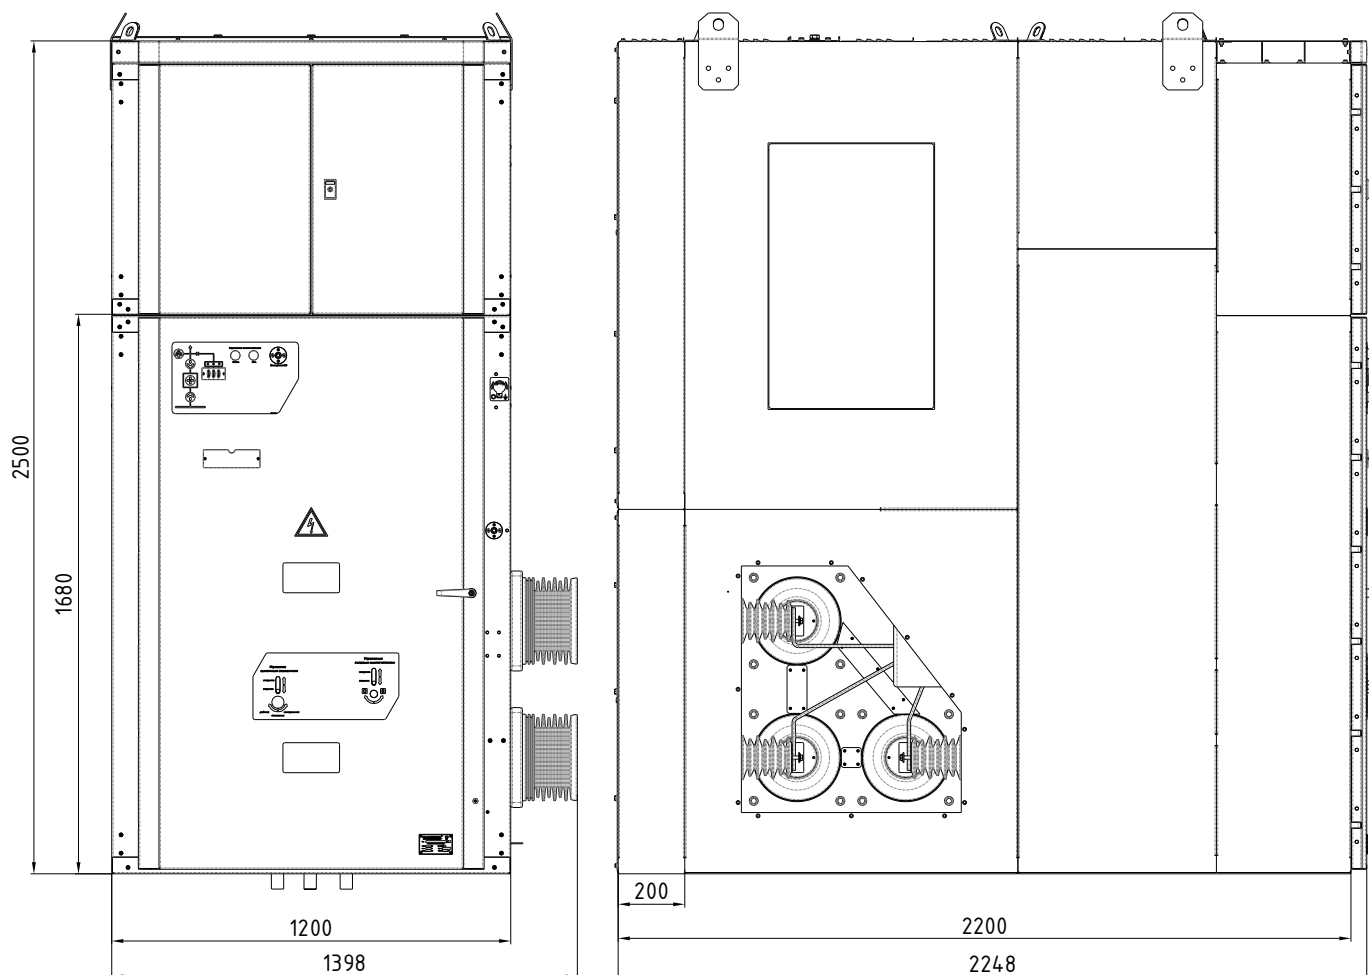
Габаритные размеры шкафов КРУ с нижним расположением сборных шин
